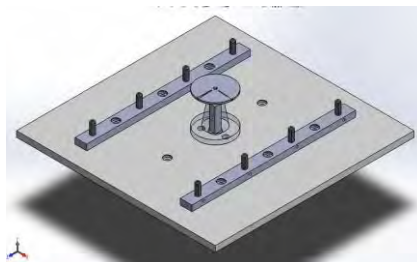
Ensamble de todos los componentes de la máquina hecho en SolidWorks.
